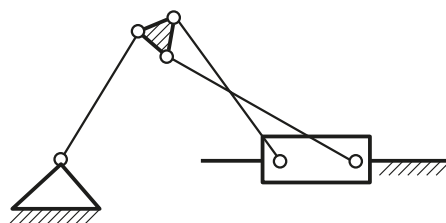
Кривошипно-ползунный механизм с двумя шатунами
